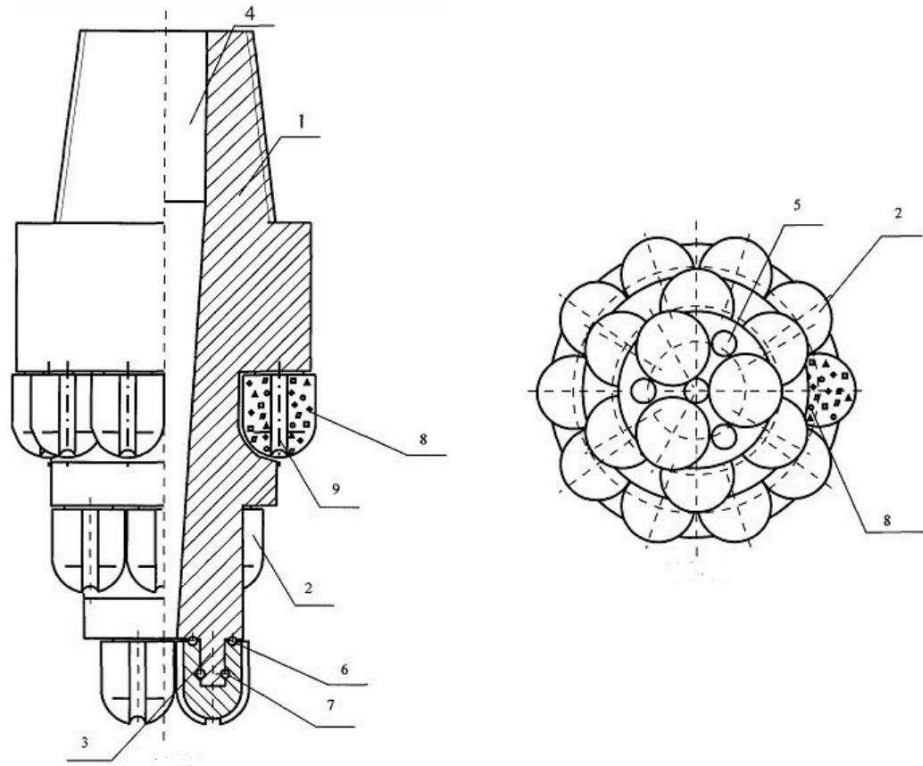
Долото з породоруйнівними елементами, що обертаються навколо власної осі (патент України 69062): 1 – корпус; 2 – породоруйнівні сателіти; 3 – осі обертання; 4 – центральний промивальний канал; 5 – бокові промивальні канали; 6 – підшипники; 7 – замки; 8 – породоруйнівні елементи; 9 – охолоджуючі промивальні канали
